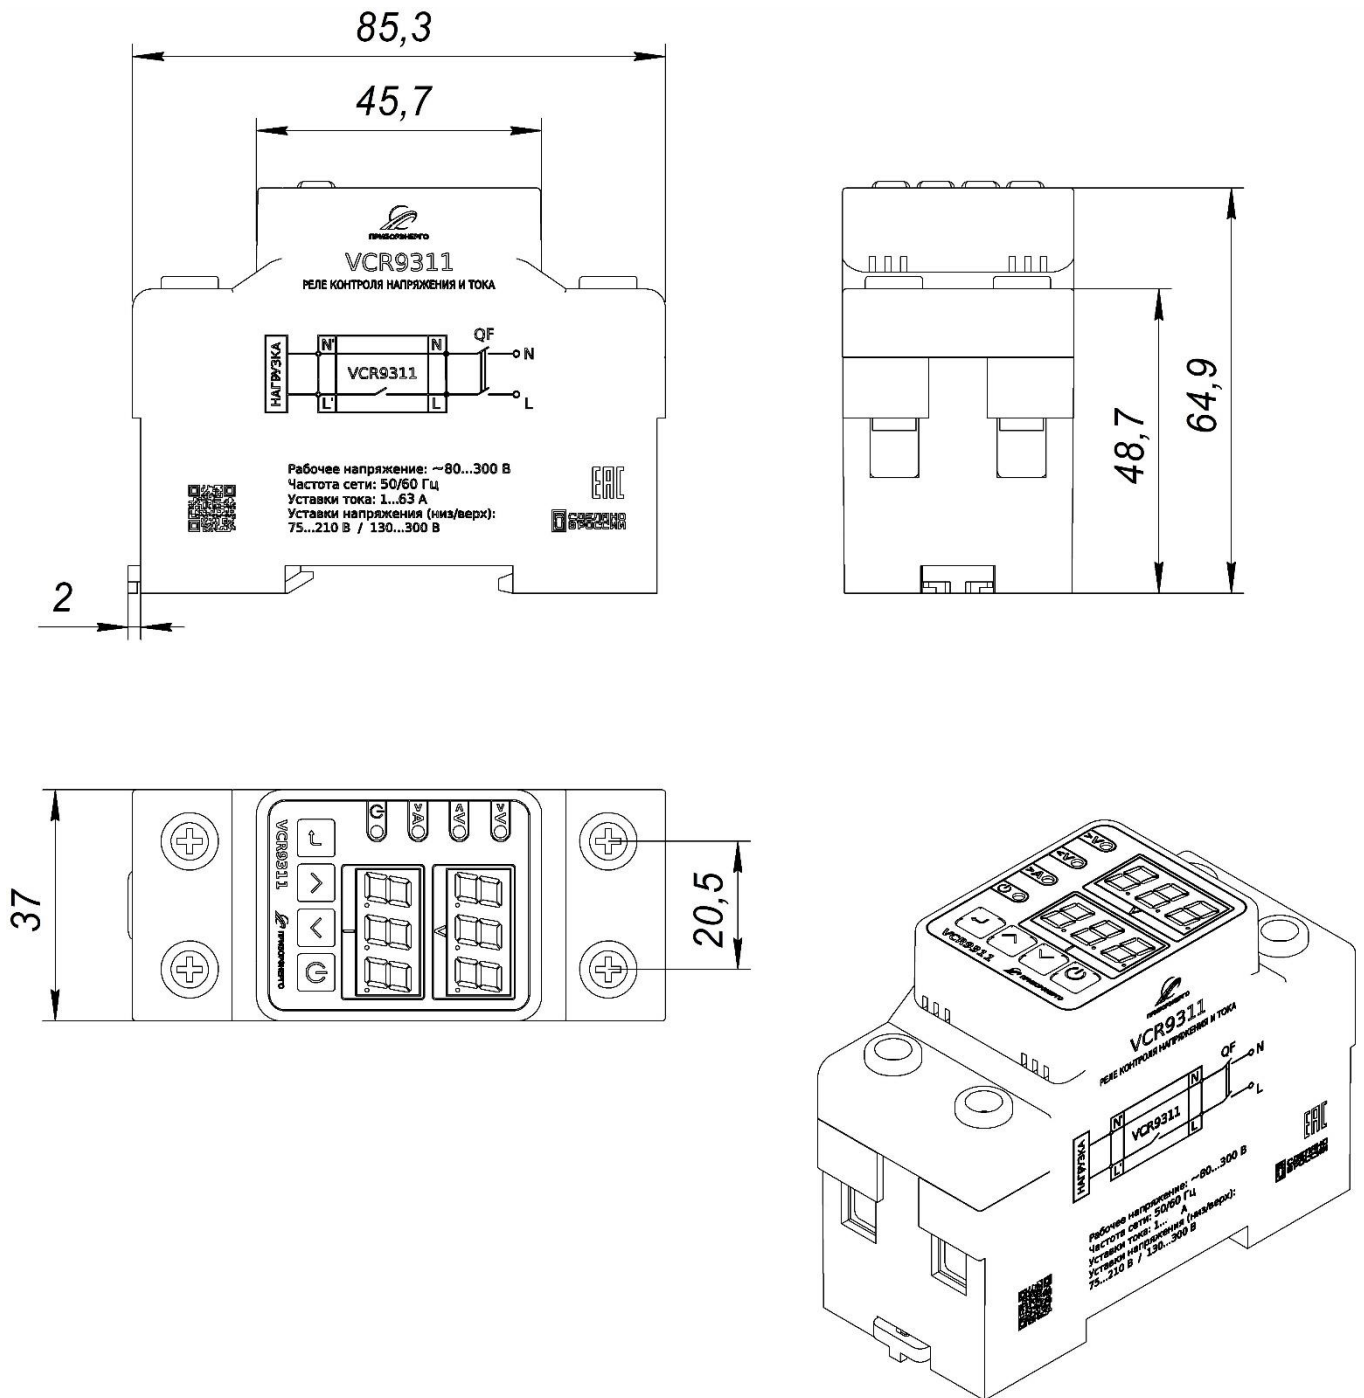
Габаритные размеры реле контроля напряжения и тока VCR9311
